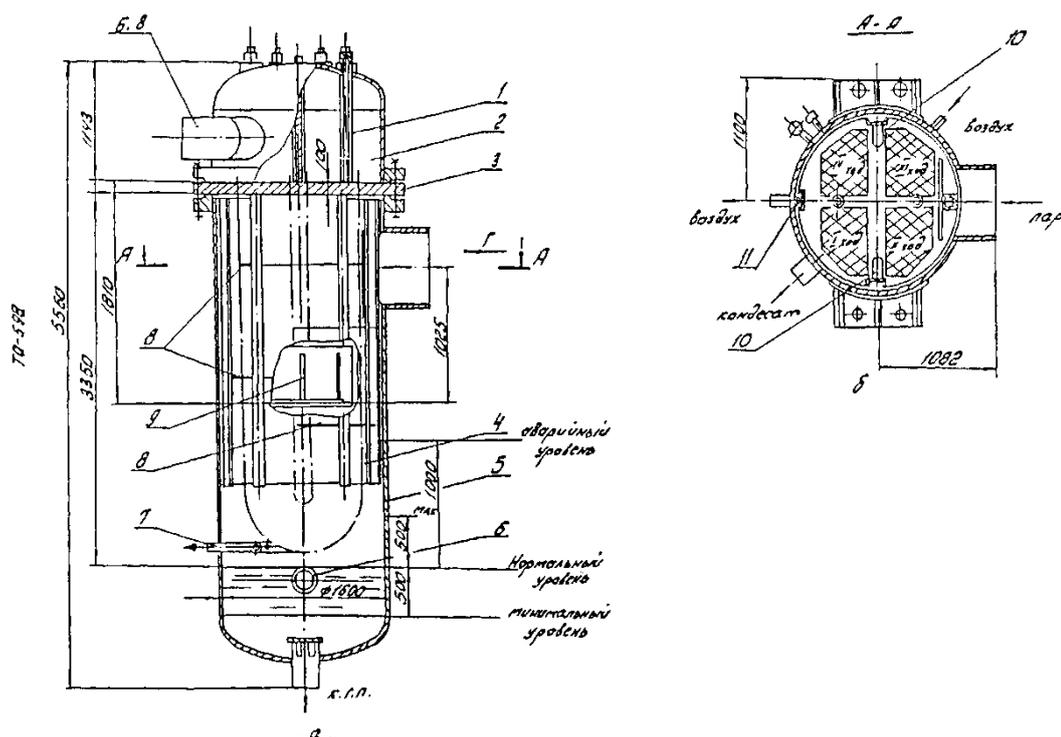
Подогреватель низкого давления типа ПН-400-26-7-11 для турбоустановок К-300-240:
